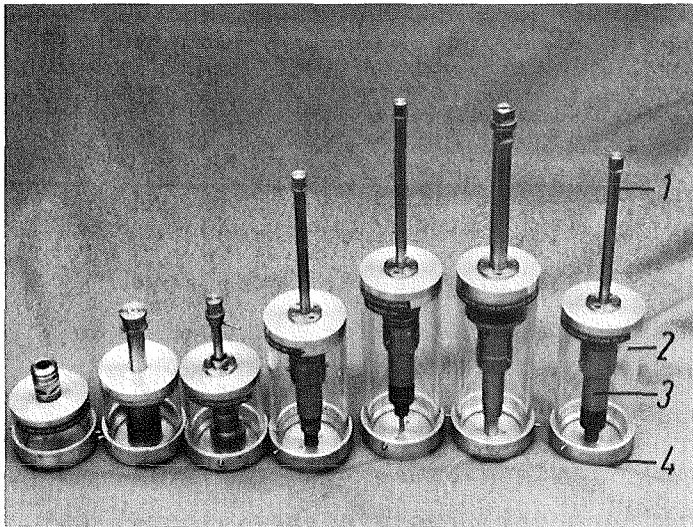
Werkzeugbehälter mit Werkzeugvorrichtungen
